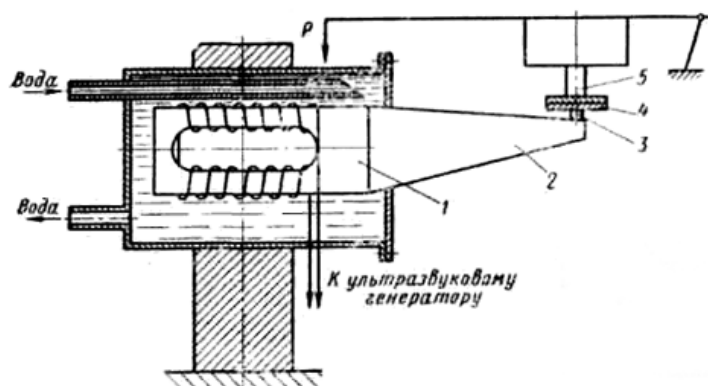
Схема сварки с использованием ультразвука: 1 – вибратор, 2 – волновод, 3 – выступ, 4 – свариваемое изделие, 5 – зажим.
